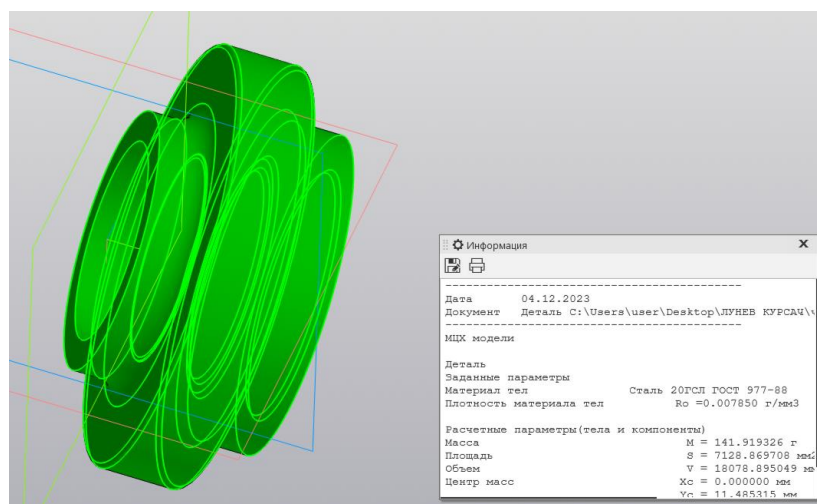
3D модель заготовки «Крышка» с массо-центровочными характеристиками
